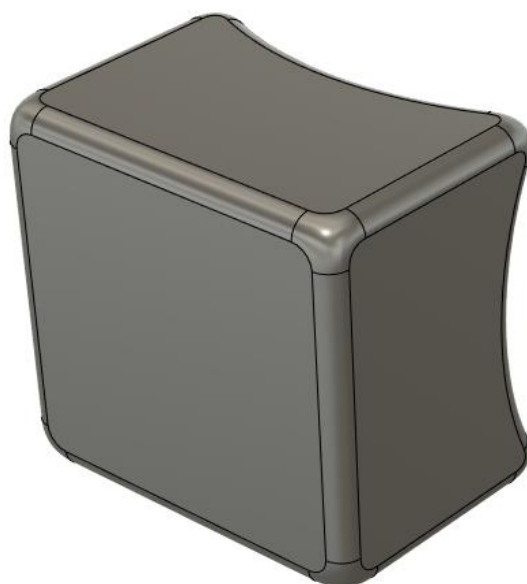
| Elaboración propia | Vista frontal de la pieza central con las esquinas redondeadas
